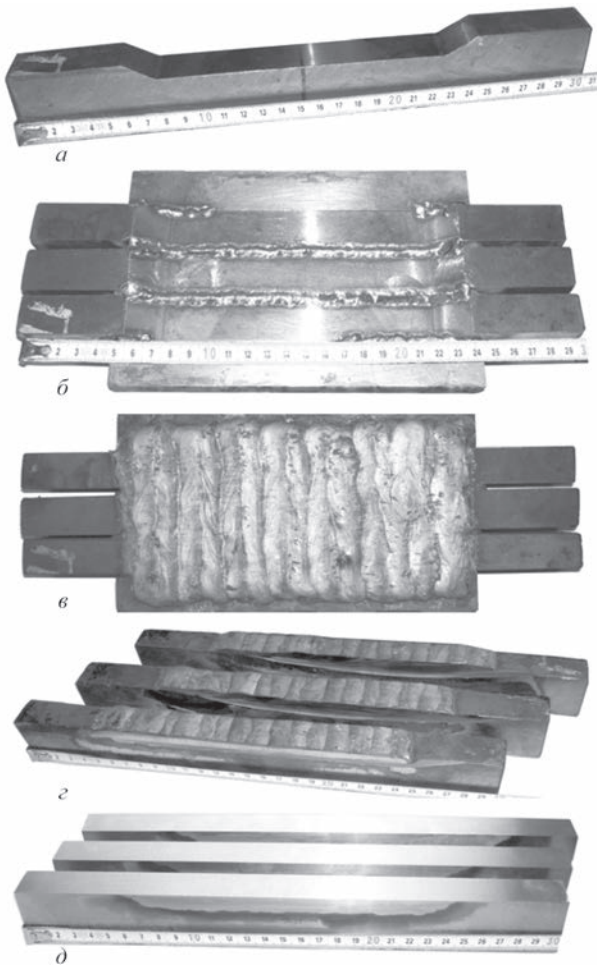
Этапы изготовления наплавленных образцов: заготовка с разделкой под наплавку (а); заготовки, собранные в пакет (б), после наплавки (в), порезки (г) и финишного шлифования (д)
